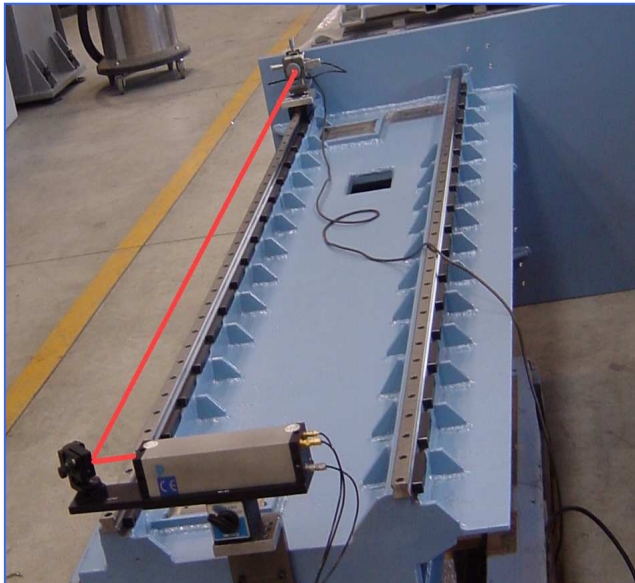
Montaggio e allineamento di una guida a ricircolo di sfere (o rulli)
